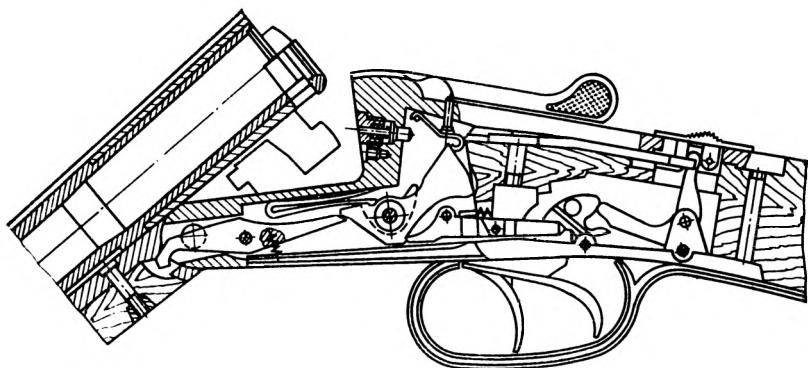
Схема устройства ударно-спускового и предохранительного механизмов ружья ИЖ-26
